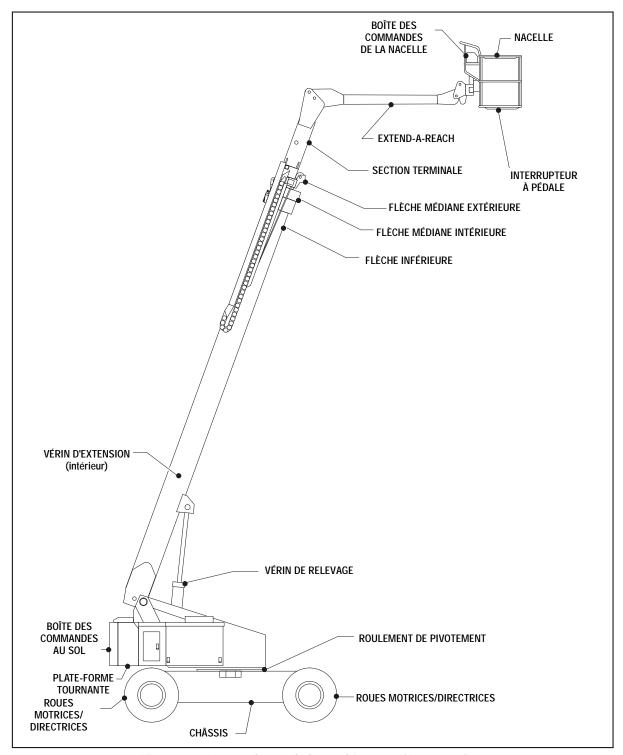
Nomenclature de la machine - 110SXJ et 120SXJ
